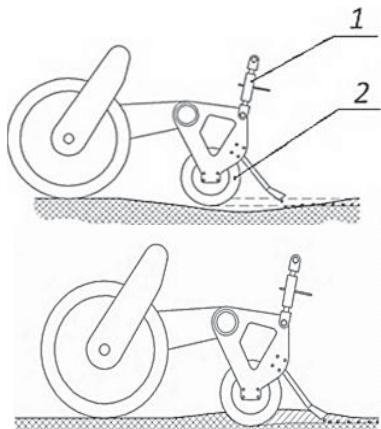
Работа бороздкоформирующего катка на неравномерной поверхности: 1 – винтовой механизм регулировки; 2 – бороздкоформирующий каток
